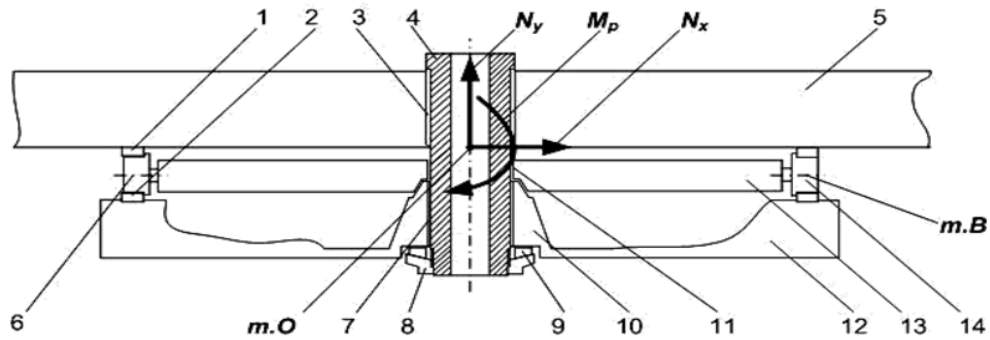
Схема общей конструкции опорно-поворотного устройства и расположения реакций связей: 1 – верхний рельс, 2 – нижний рельс, 3 – втулка (верхний и нижний пояса) поворотной платформы, 4 – центральная цапфа, 5 – поворотная платформа, 6 – роликовый круг, 7 – втулка нижней рамы, 8 – гайка центральной цапфы, 9 – сферическая шайба, 10 – отливка нижней рамы, 11 – втулка сепаратора роликового круга, 12 – нижняя рама, 13 – сепаратор роликового круга, 14 – передний ролик (точка В), N_x - горизонтальная составляющая нагрузок, N_y – вертикальная составляющая нагрузок, M_p – реактивный (изгибающий) момент.
